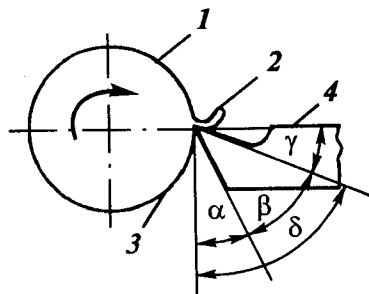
Схема процесса резания на токарном станке: 1 — обрабатываемая поверхность; 2 — стружка; 3 — обработанная поверхность; 4 — резец
